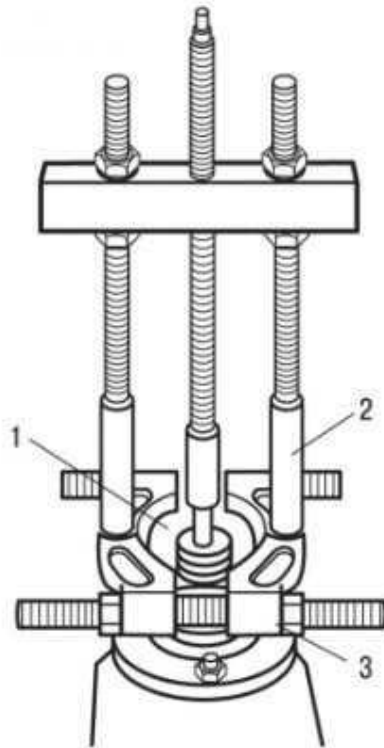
Зняття внутрішньої обойми підшипника:
